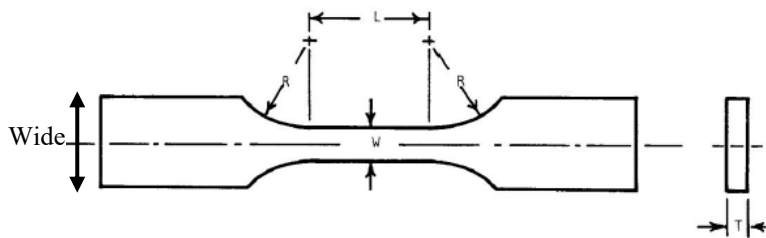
Éprouvette standard selon la ASTM E466 [72]
